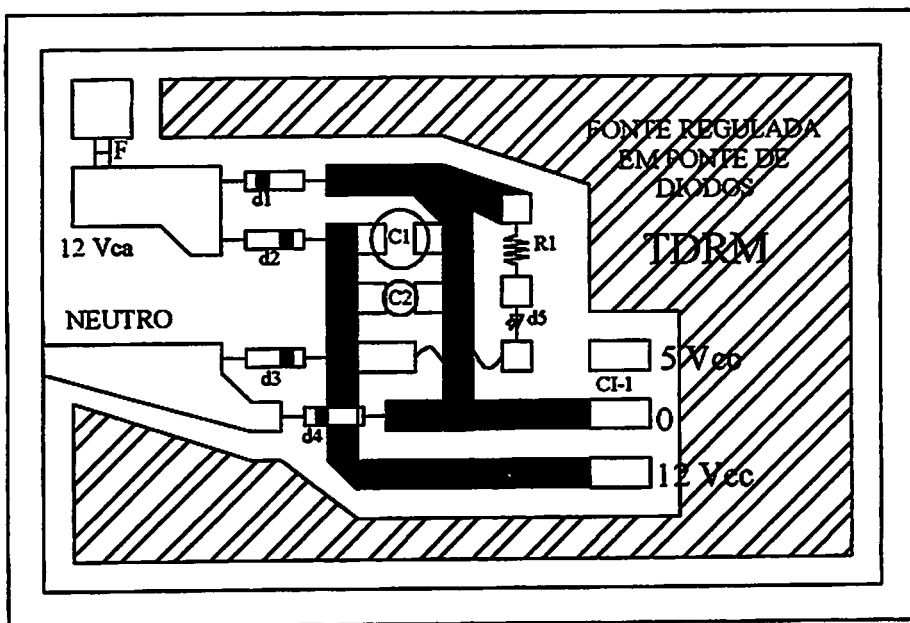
A: Projeto técnico da placa de circuito impresso para montagem do controlador de irrigação.
